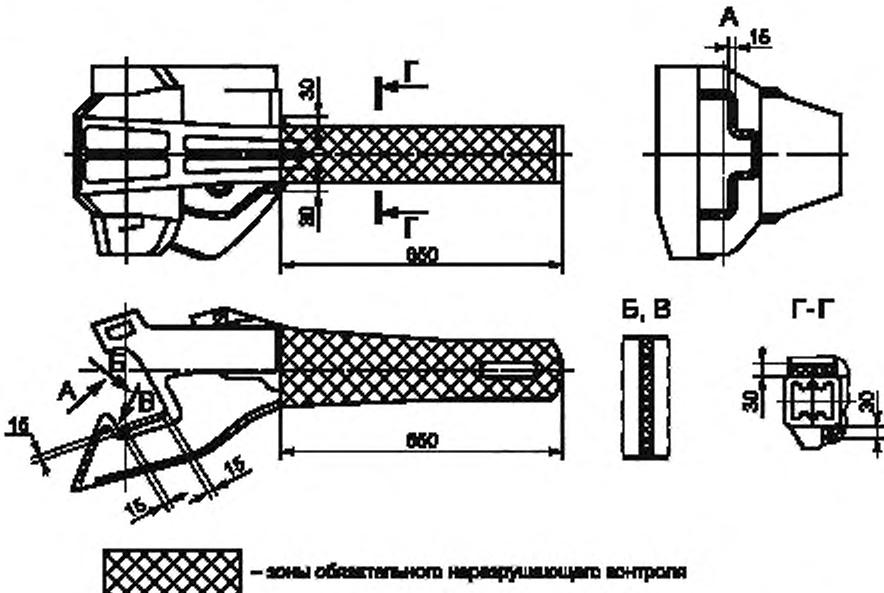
а) — Зоны неразрушающего контроля на корпусах автосцепок СА-3
